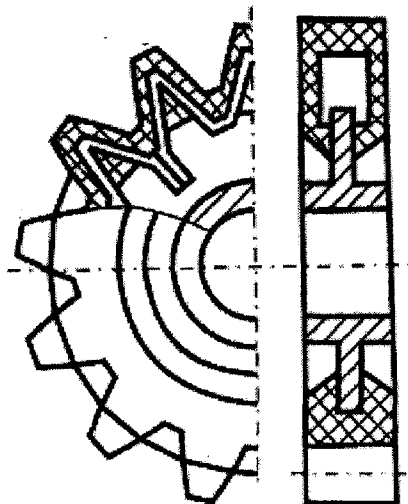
Полимерное зубчатое колесо с ленточной металлической арматурой в теле зуба [2]
